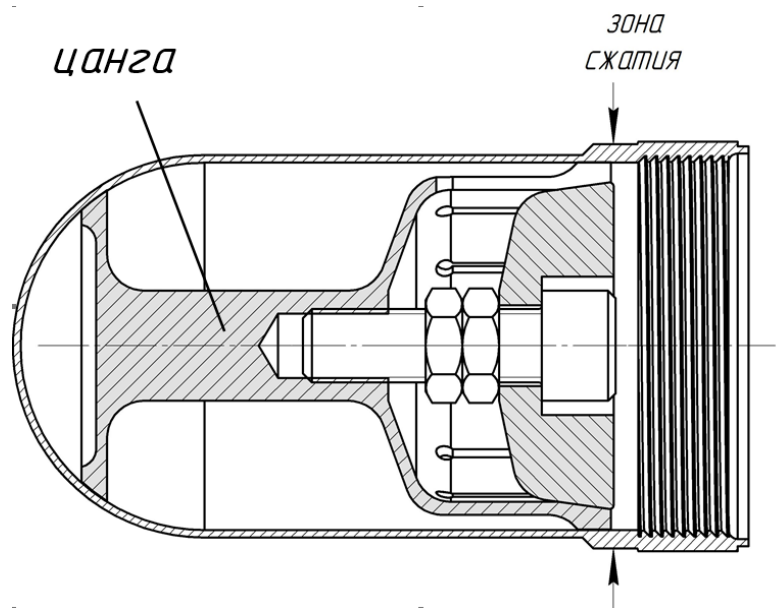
Схема установки разжимной цанги в оболочечном корпусе
